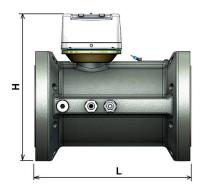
Dimensiones del cuerpo de aluminio del iM-TM
